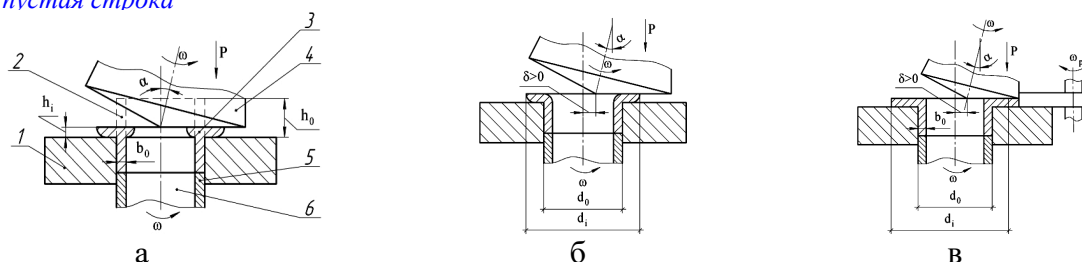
Схемы высадки раскаткой буртов (1 – матрица; 2 – заготовка; 3 – изделие; 4 – валок; 5 – выталкиватель; 6 – оправка):
